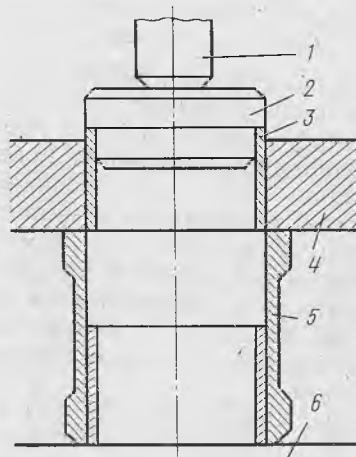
Схема для перемещения свернутой пластины из пресс-формы в деталь:
